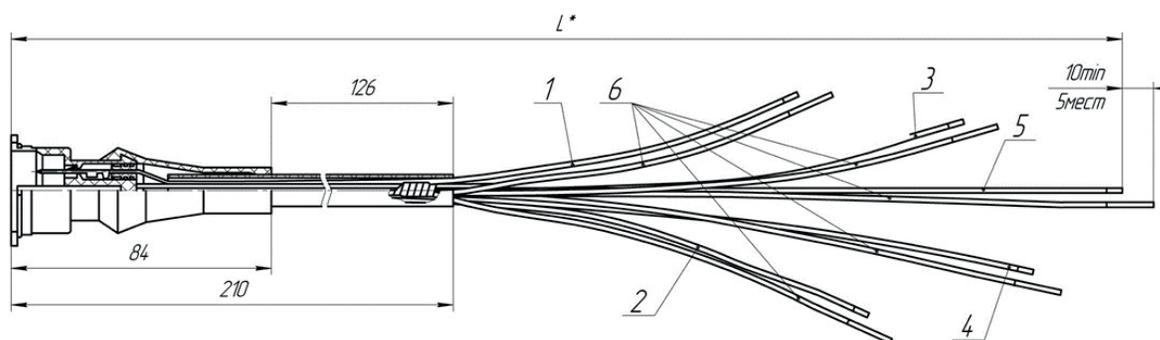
Вилка с армированными проводами СЦАЗ-2-6-Р
